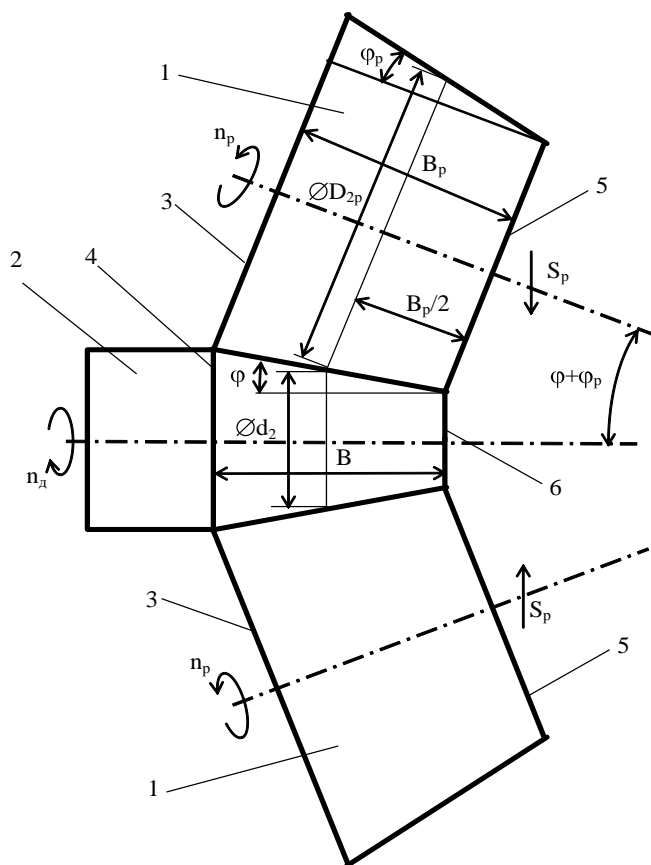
Схема накатывания конической резьбы коническими роликами со скрещивающимися осями инструмента и заготовки
